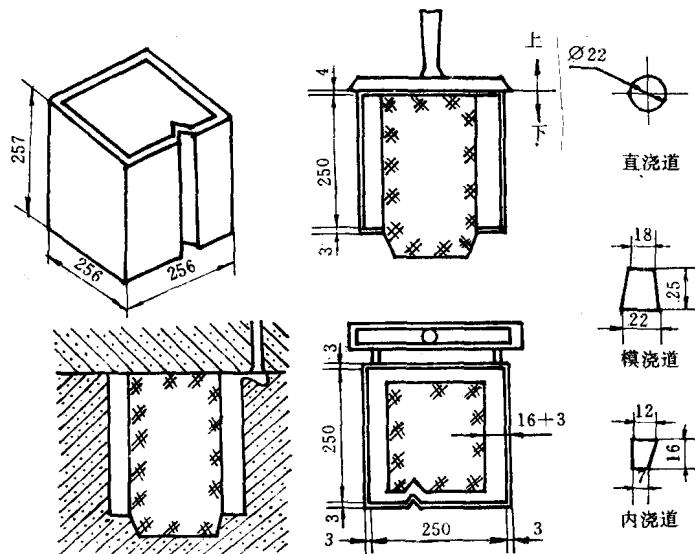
4 方箱铸件图、铸造工艺图、铸型装配图
